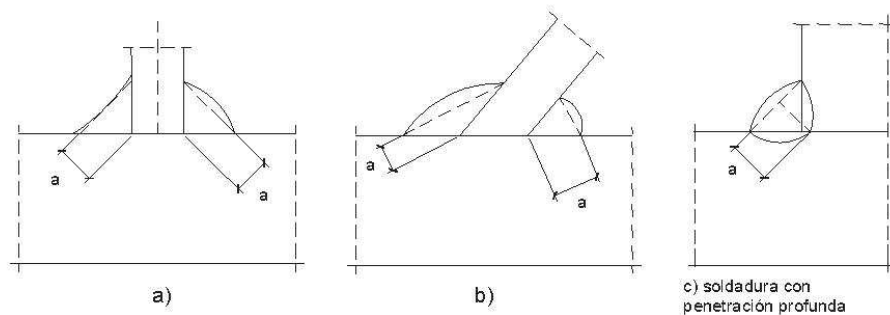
Soldadura en ángulo. Espesor de garganta
